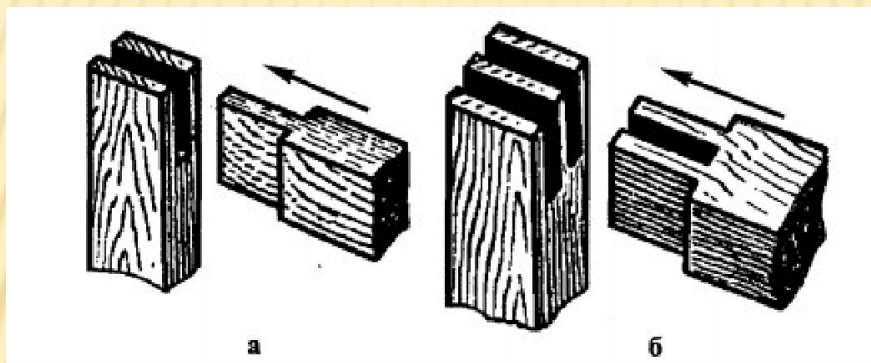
Шиповое соединение деталей: а — одинарным шипом; б — двойным шипом
